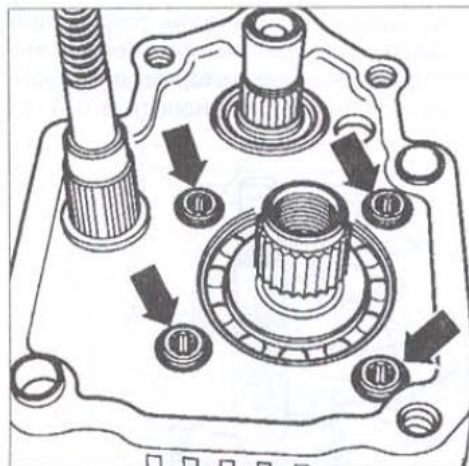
Розташування гвинтів кріплення фіксатора підшипника вхідного вала
